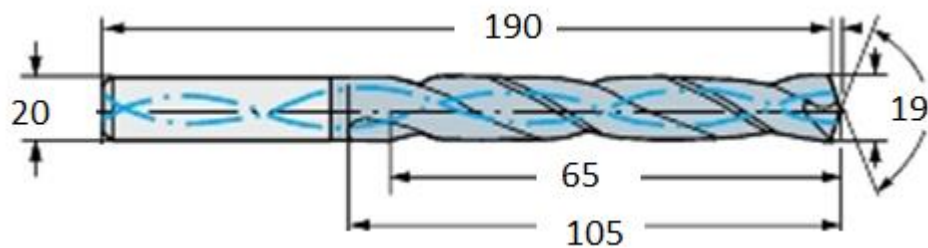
сверло Sandvik Coromant CoroDrill 460.1-1900-143A1-XM GC34
